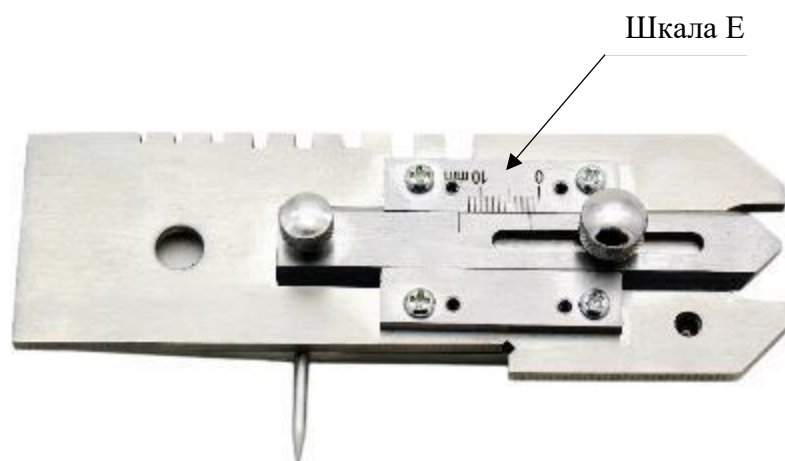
Общий вид шаблона сварщика универсального УШС-4
